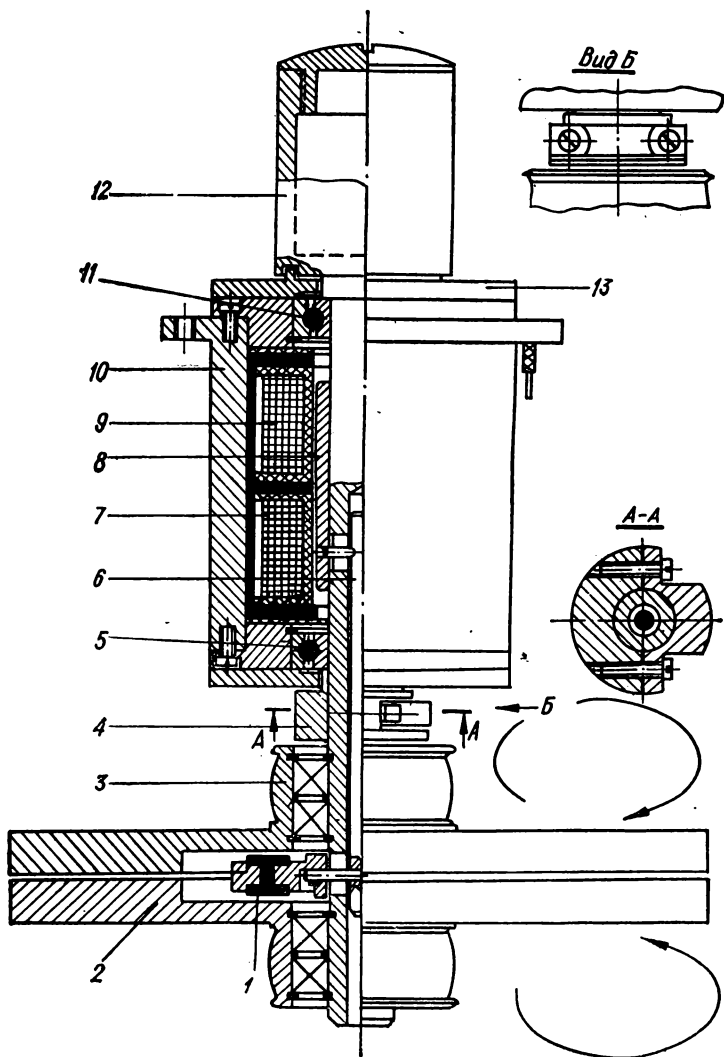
Реверсивный узел ведущего вала исполнения II старт-стопного МТЛ.
